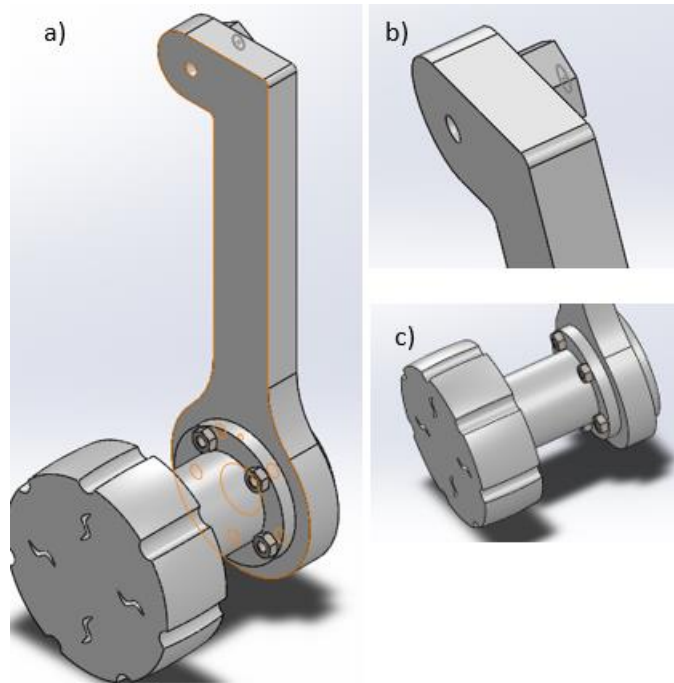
a) Eslabón conector viga #3. b) Hexágono para realizar ensamble con viga. c) Ensamble llanta eslabón.
